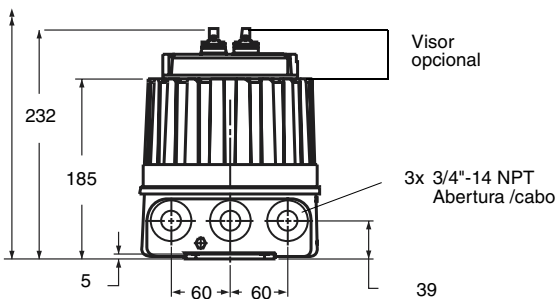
Dimensões do transmissor RFT9739 de montagem em campo
